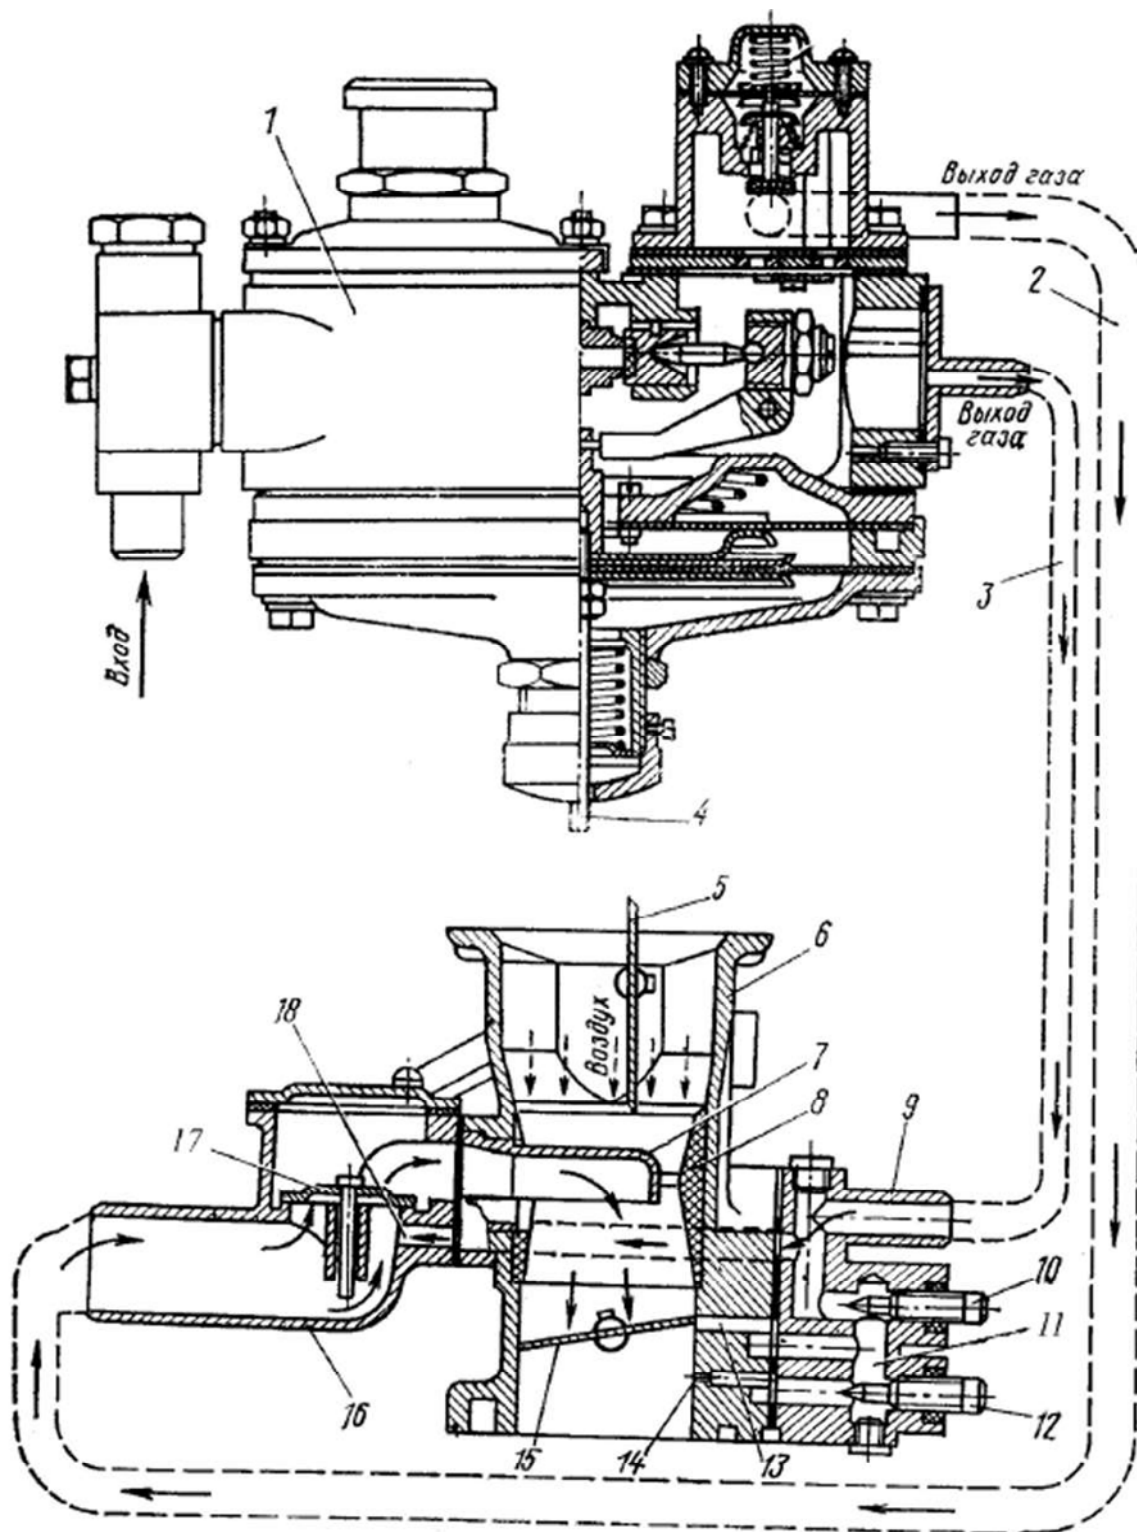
Схема газового смесителя и его соединения с газовым редуктором: 1- корпус газового редуктора; 2 - шланг подвода газа к главной дозирующей системе смесителя; 3 - трубка подвода газа к системе холостого хода смесителя; 4 - стержень диафрагмы второй ступени редуктора; 5 - воздушная заслонка; 6- корпус смесителя; 7 - газовая форсунка; 8 - диффузор; 9 - крышка с патрубком подвода газа и каналами системы холостого хода смесителя; 10, 12 - винты регулировки работы смесителя при холостом ходе; 11, 18 - каналы; 13, 14 - отверстия для выхода газа при работе на малых частотах холостого хода; 15 -
